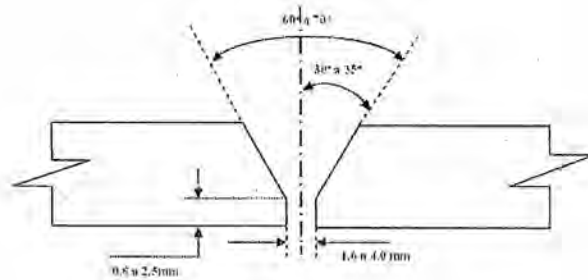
Tolerancias para chanfles de Juntas Soldadas en cañerías
